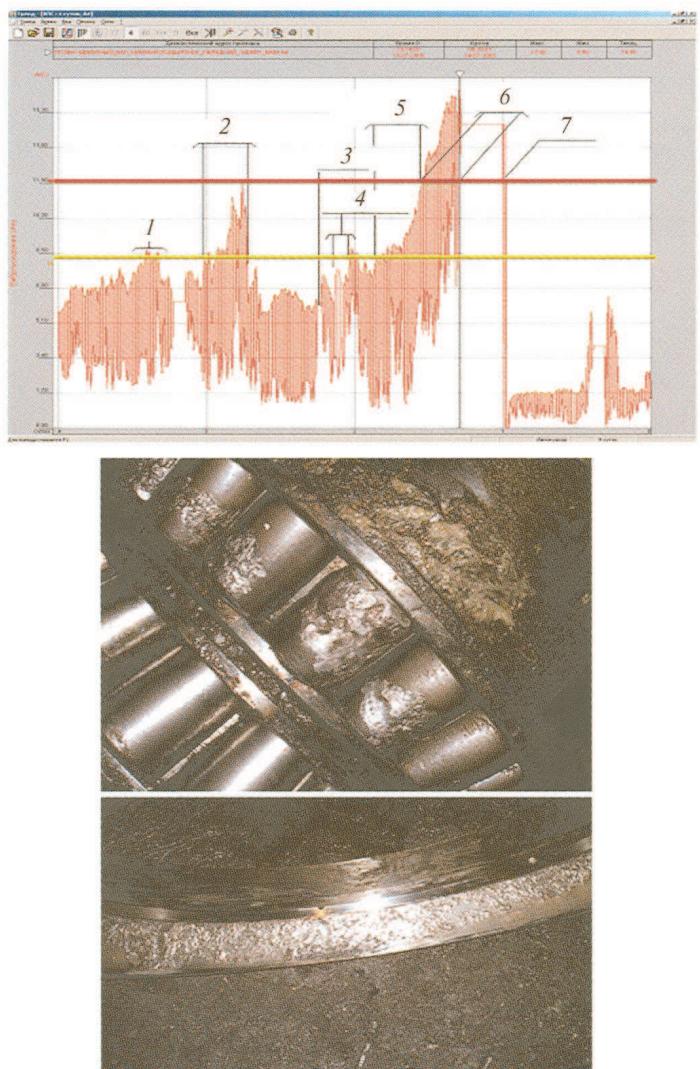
Тренд вибропараметра, отвечающего за наличие или отсутствие смазки в подшипниковом узле быстроходного вала нижнего редуктора колесопрокатного стана
